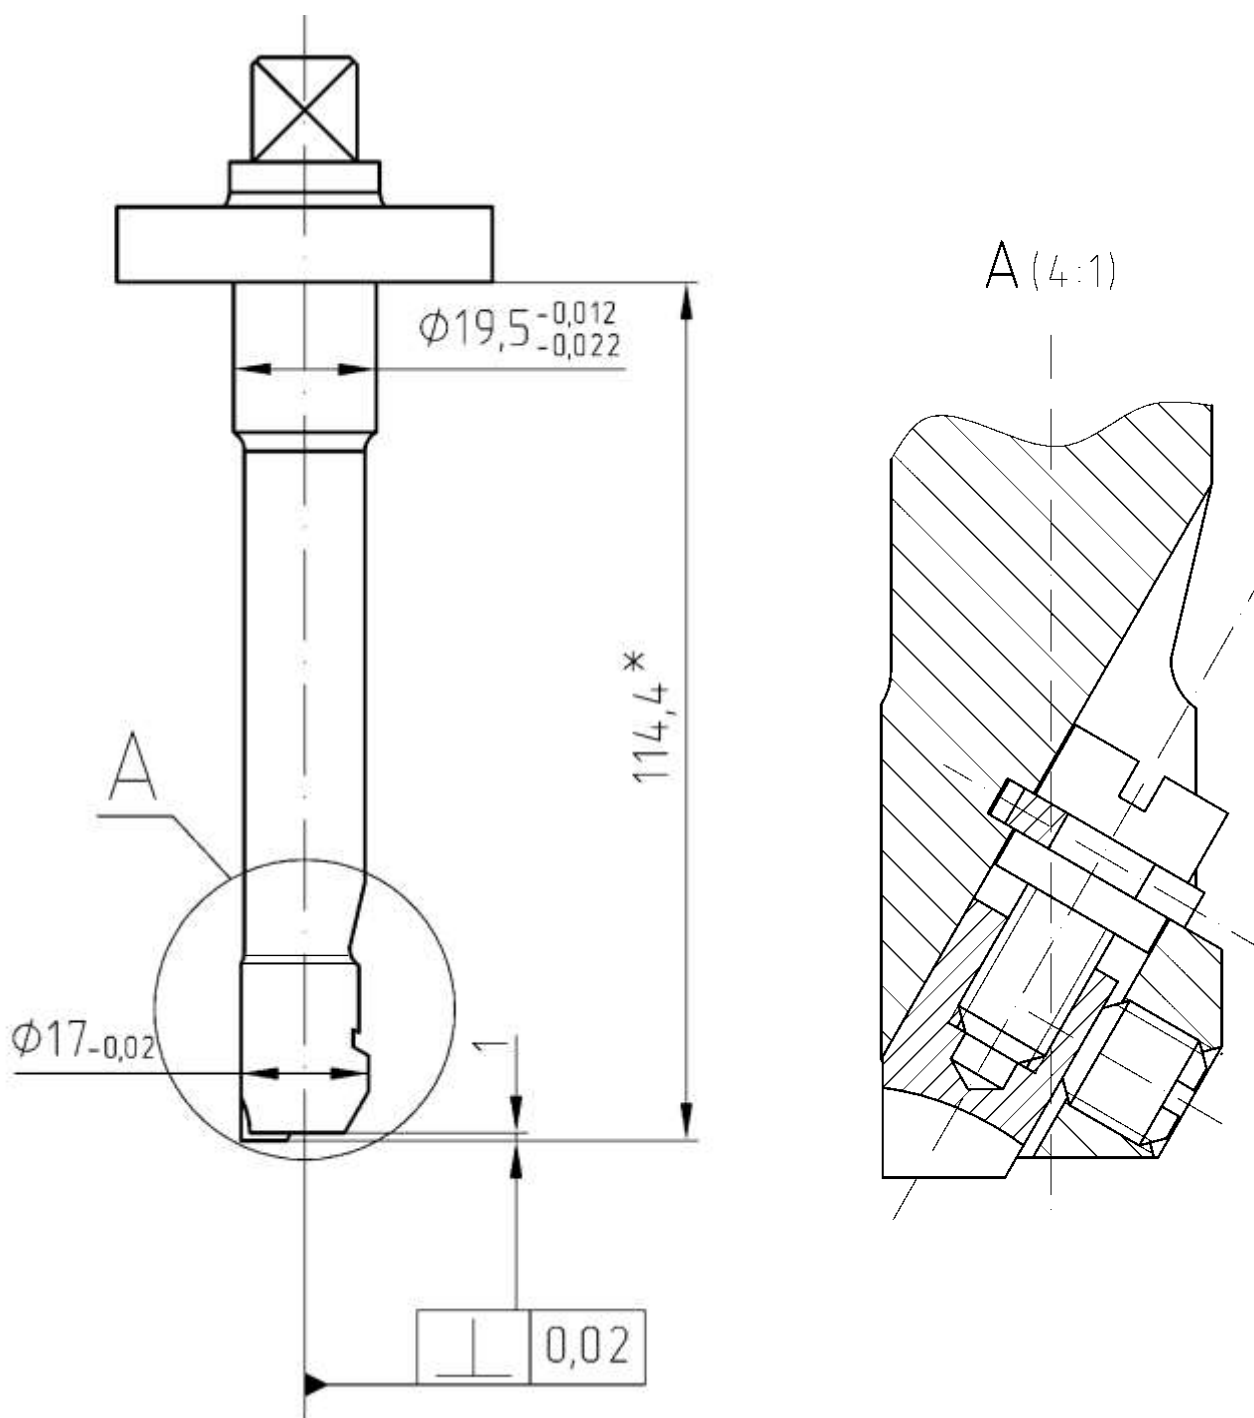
27-Ф-3871 Резец для подрезки (зачистки) торца под уплотнительное кольцо топливной форсунки
